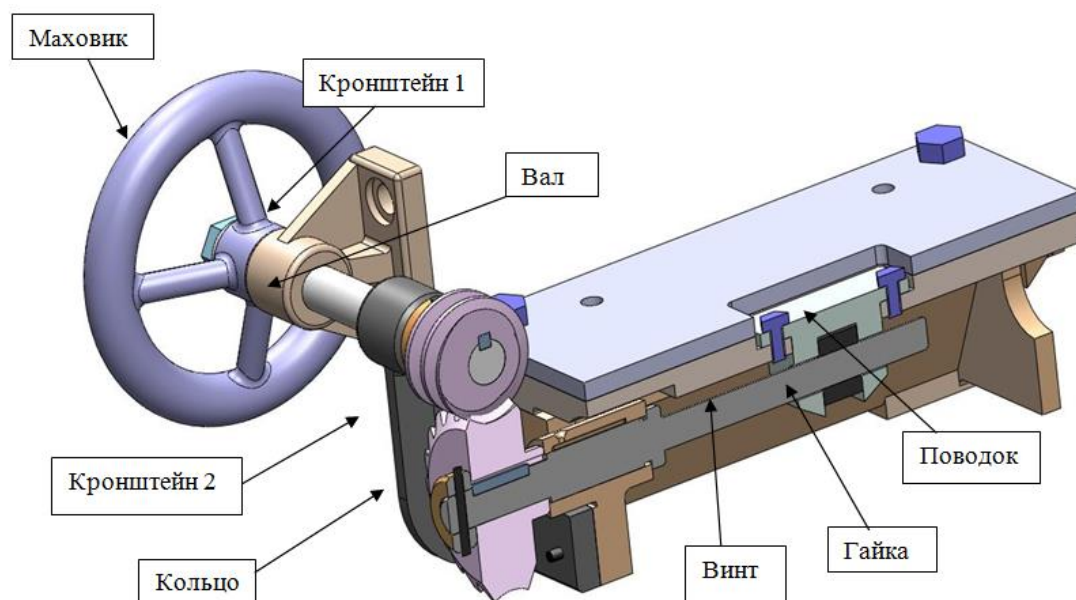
Натяжное устройство: салазки для перемещения электродвигателя
